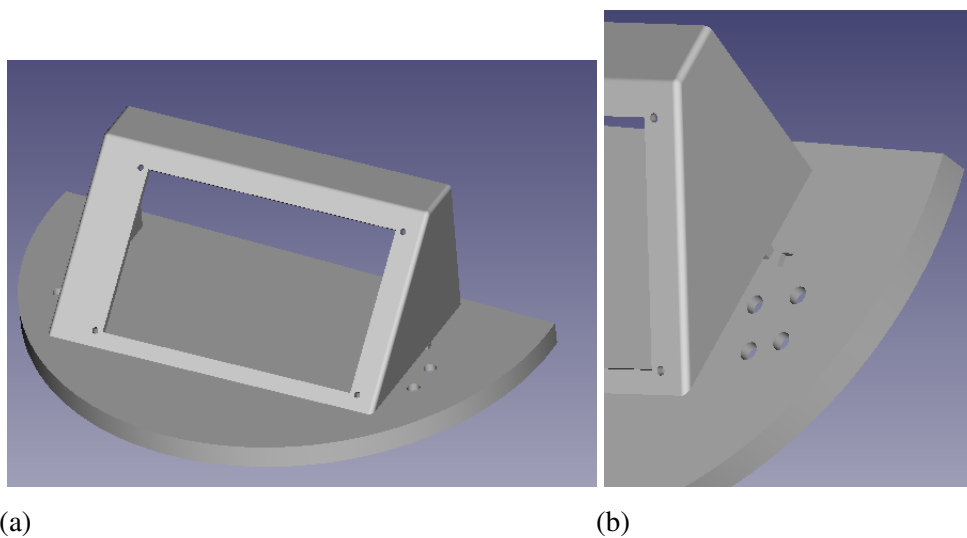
Diseño de la cabeza del robot uniendo ambas partes.
